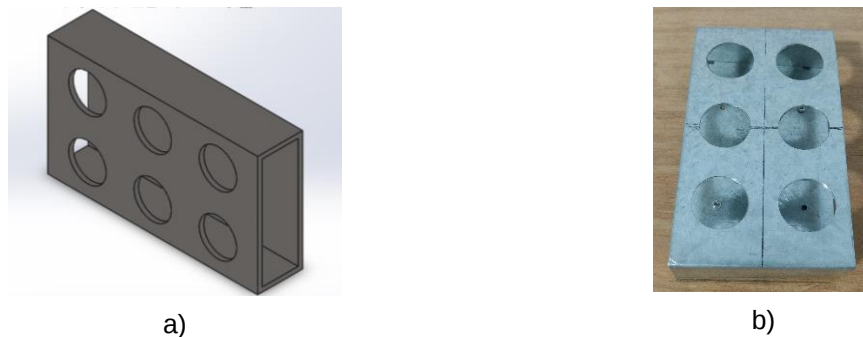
Rack de almacenamiento a) Rack diseñado en Solidworks® b) Rack construido.
